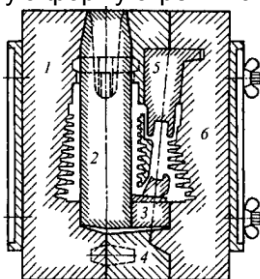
Формовка в стержнях цилиндра двигателя с воздушным охлаждением
